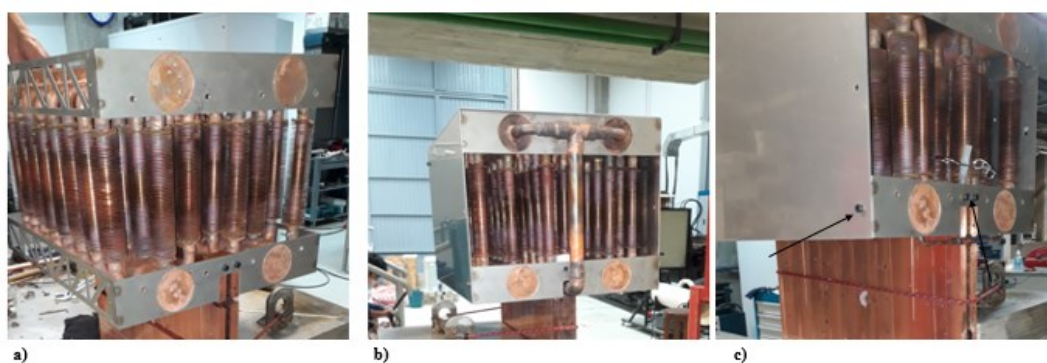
Montagem da seção de testes. a) carenagem de suporte. b) montagem completa. c) fixação por parafusos.
